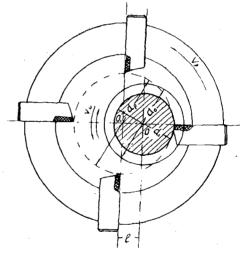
Схема охватывающего фрезерования при вращающейся детали.
